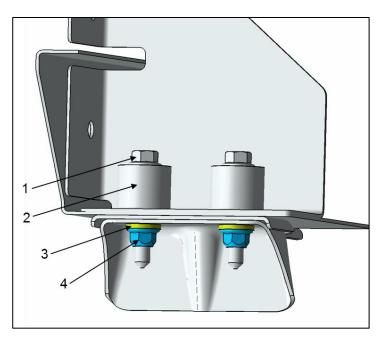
Exemple d'assemblage vissé avec élément amortisseur
